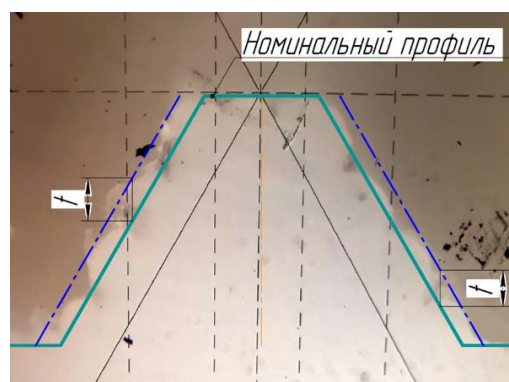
Профиль резьбы M14, сформированной в образце из PLA-пластика
